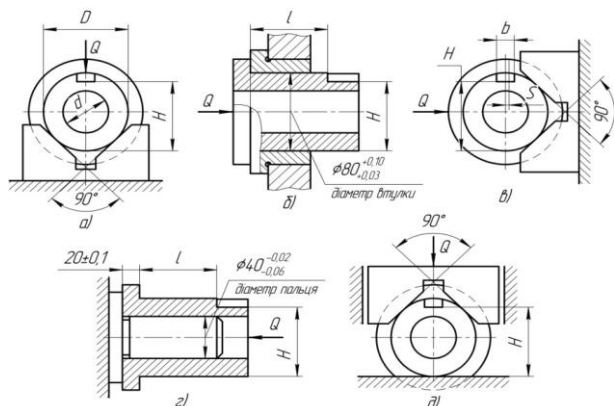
Варіанти схем встановлення втулки при фрезеруванні пазу.
